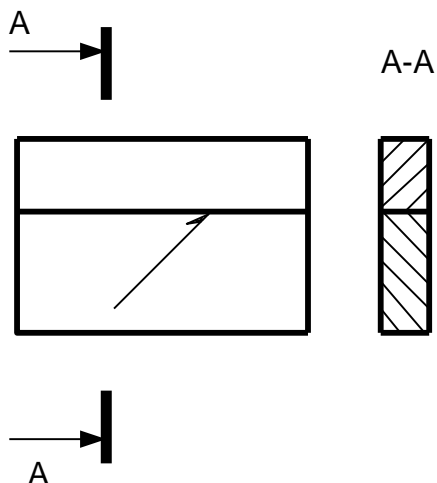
Изображение видимого шва сварочного соединения
